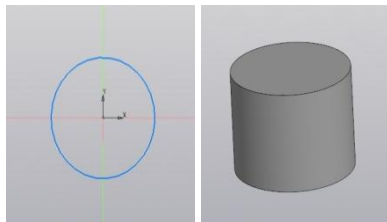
Эскиз цилиндра Рисунок 3 – Цилиндр
